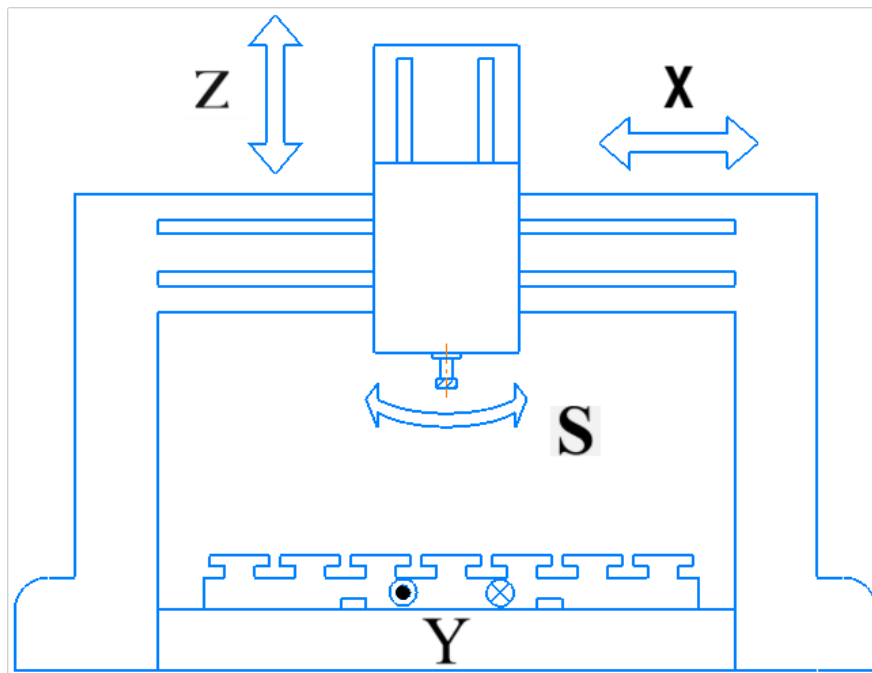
Принципиальная схема станка для обработки крупногабаритных заготовок
